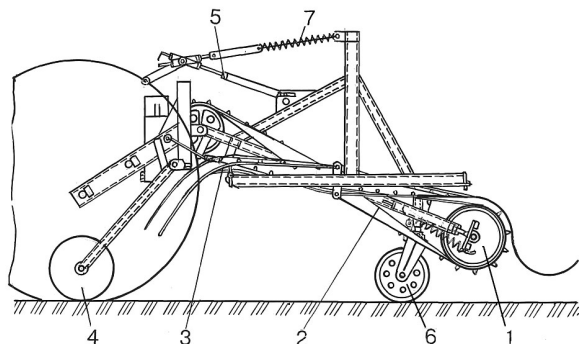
Навесной однопоточный оборачиватель ленточного типа:
